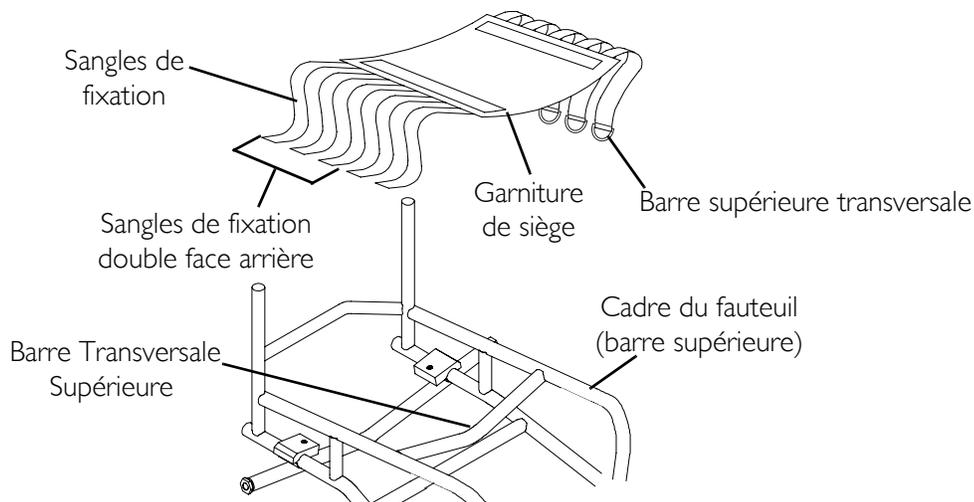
Remplacement de la garniture de siège réglable en tension
